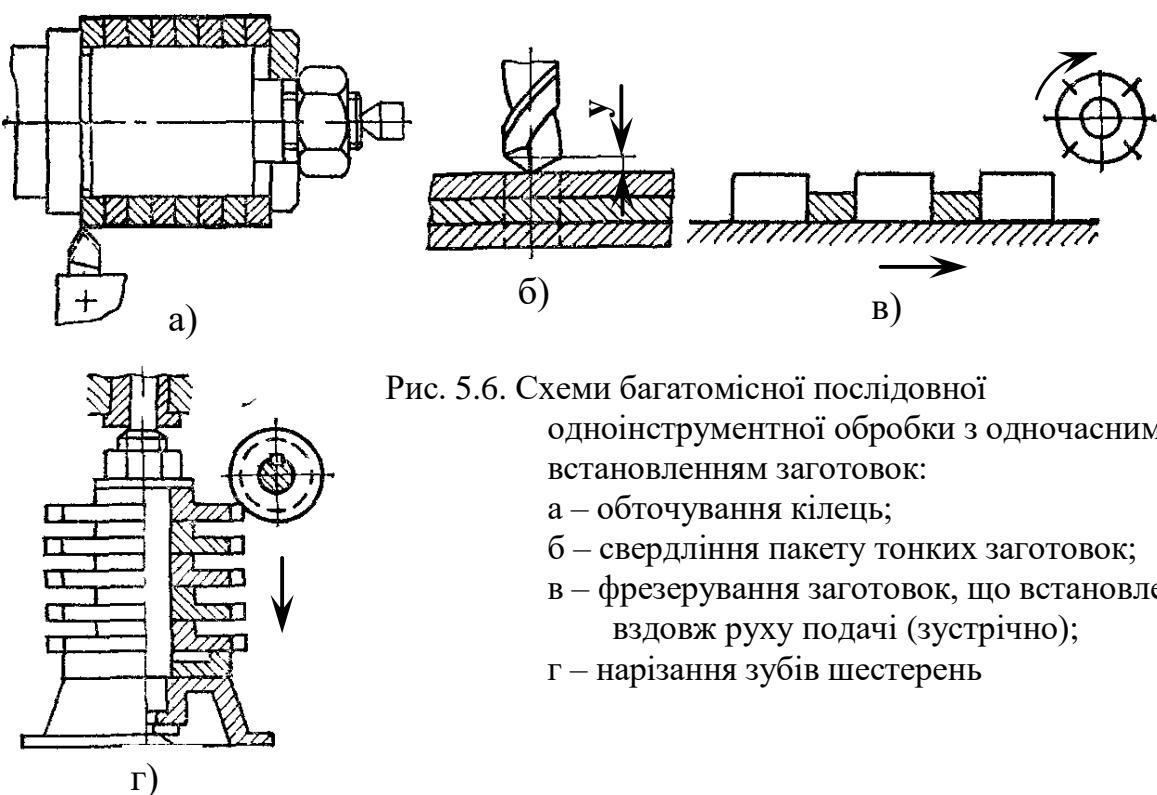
Схеми багатомісної послідовної одноінструментної обробки з одночасним встановленням заготовок:
